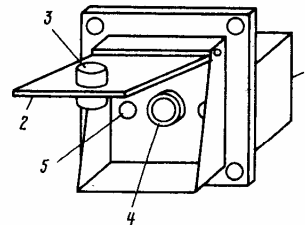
Конструкция корпуса индикаторного блока: 1 — корпус; 2 — откидная крышка; 3 — постоянный магнит; 4 — окно основного индикаторного элемента; 5 — окно аварийного индикаторного элемента
